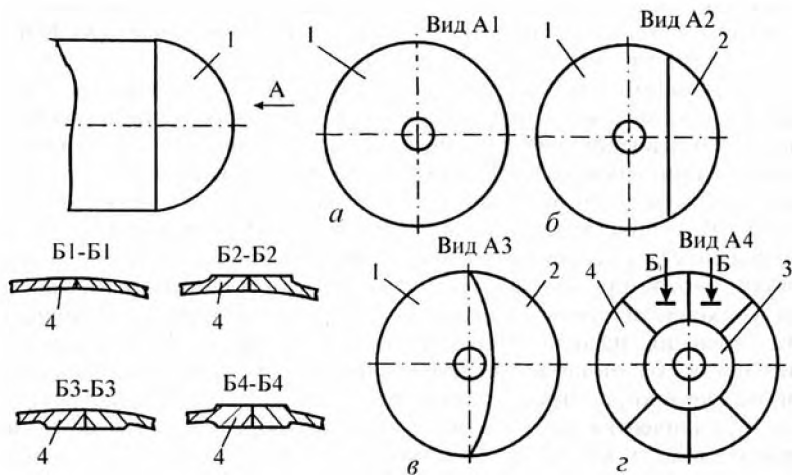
Днища баков: 1 – днище; 2 – часть днища; 3 – полусная часть; 4 – лепесток; Б1-Б1, Б2-Б2, Б3-Б3, Б4-Б4 – варианты сварных соединений
